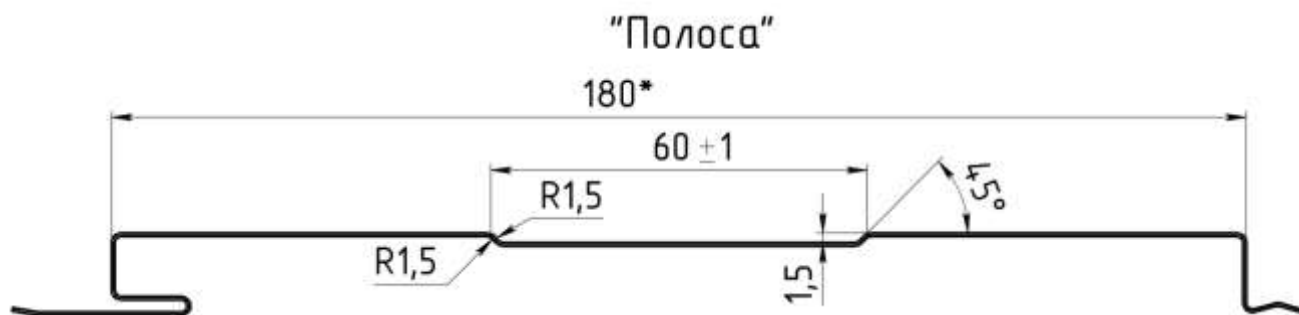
Фасадно-облицовочная панель с отделкой «Полоса»
